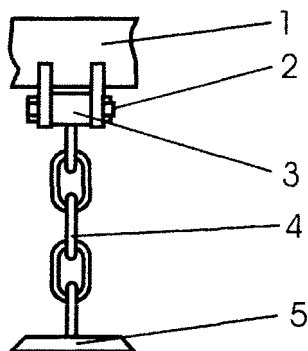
Конструктивная схема рабочего органа косилки-измельчителя КИ-3
